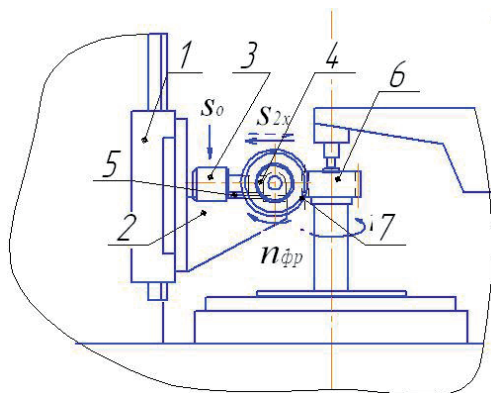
Робоча зона зубофрезерного верстата з автоматизованим приводом зворотно-поступального руху дискової фрези на основі РК-способу: 1 — інструментальний супорт; 2 — консоль; 3 — кроковий двигун; 4 — серводвигун приводу головного руху; 5 — каретка з напрямними; 6 — заготовка зубчастого колеса; 7 — дискова фреза
